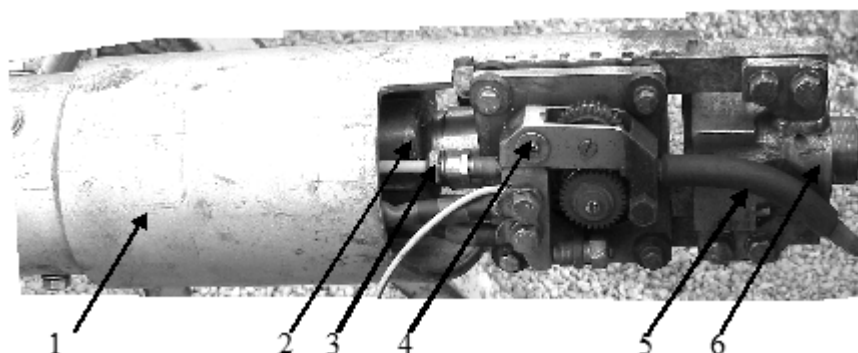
Автомат для сварки в стеснённых условиях на большой глубине:
